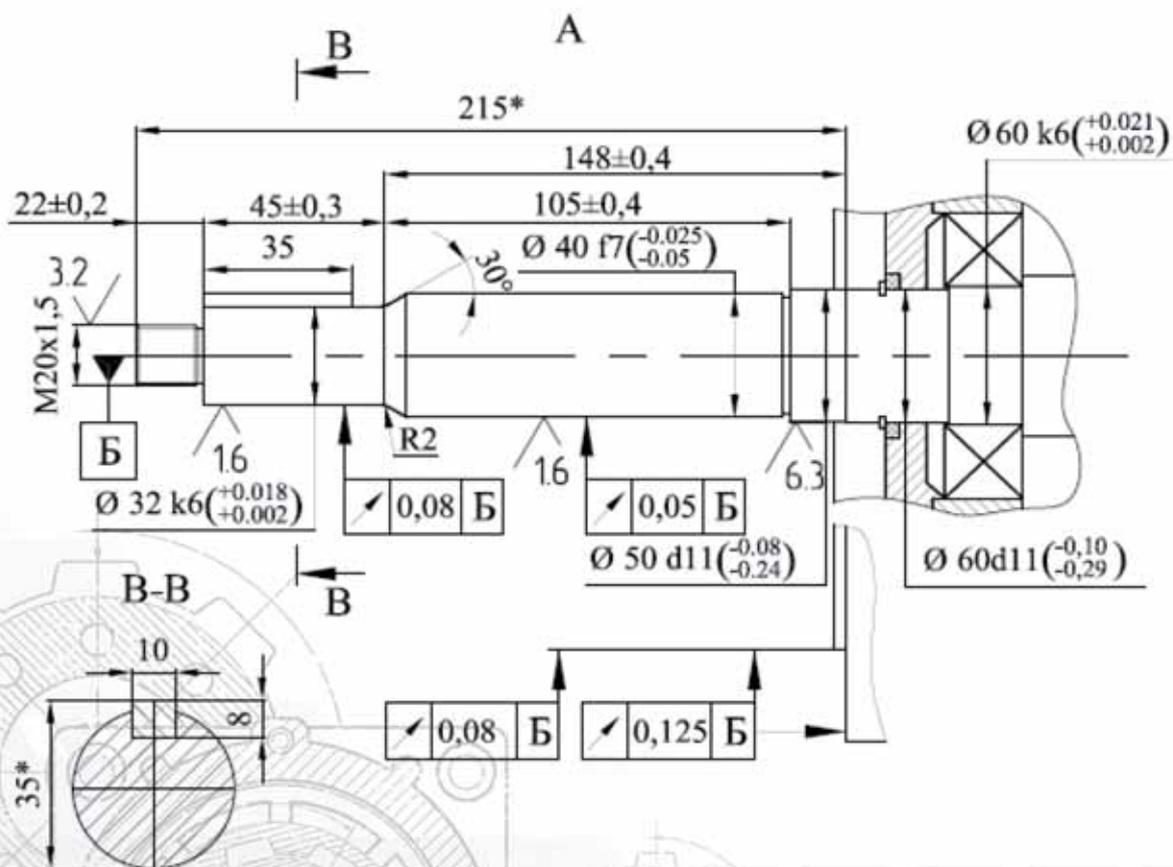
Свободный конец вала двигателя 6АМУ180М2ЖУ2
